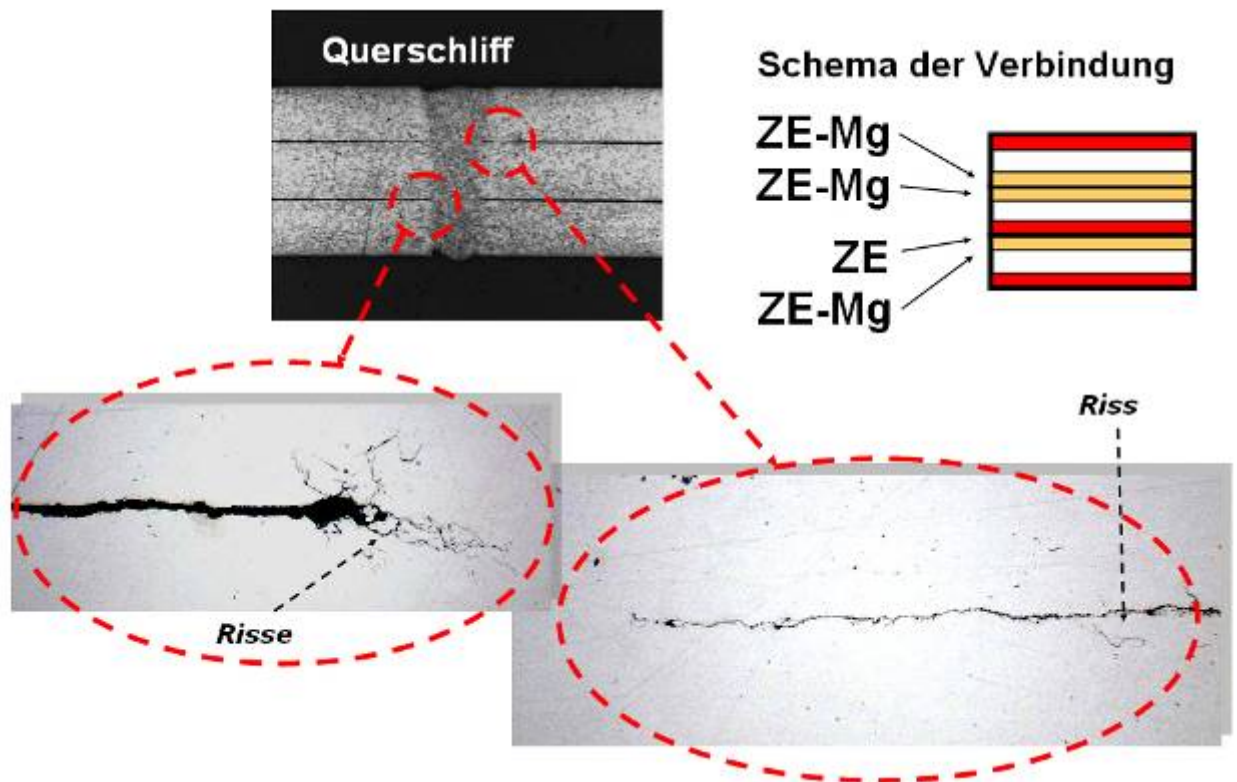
Mikrorisse im Schweißgut und in der WEZ einer Laser-Schweißnaht an den ZE-Mg-beschichteten Blechen von H220Y, Variante 5 (Mikroaufnahmen: poliert und ungeätzt)
